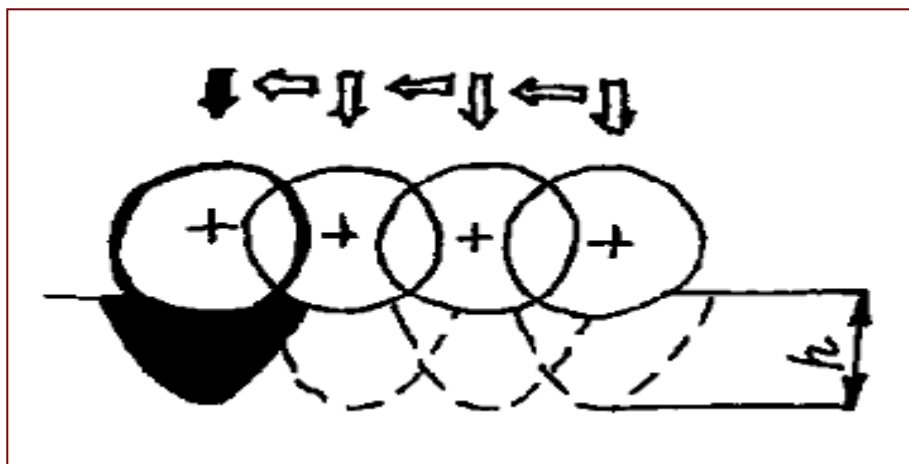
Схема обробки поверхневою пластичною деформацією при ударній дії інструменту
